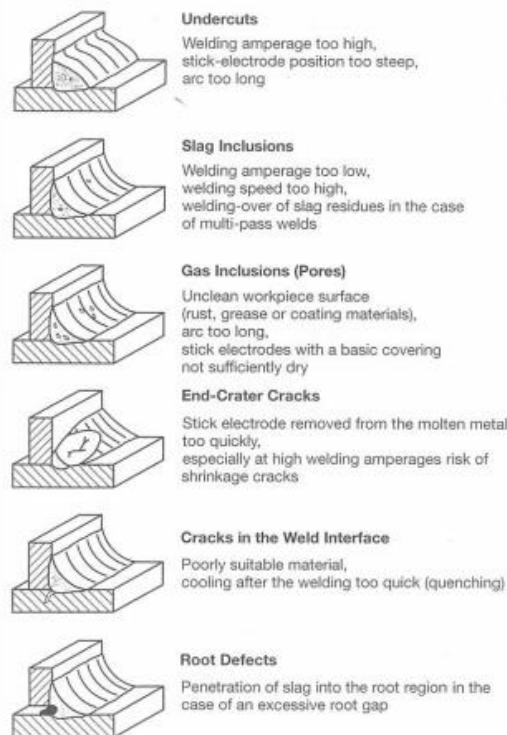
Defeitos (irregularidades) da soldadura e suas possíveis causas, retratado através do uso de uma soldadura de canto com exemplo, [2].
